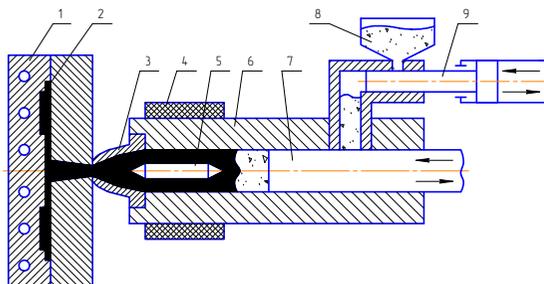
Схема литья под давлением: 1 – пресс-форма; 2 – изделие; 3 – сопло; 4 – электронагреватель; 5 – рассеиватель; 6 – рабочий цилиндр; 7 – поршень; 8 – загрузочный бункер; 9 – дозатор
